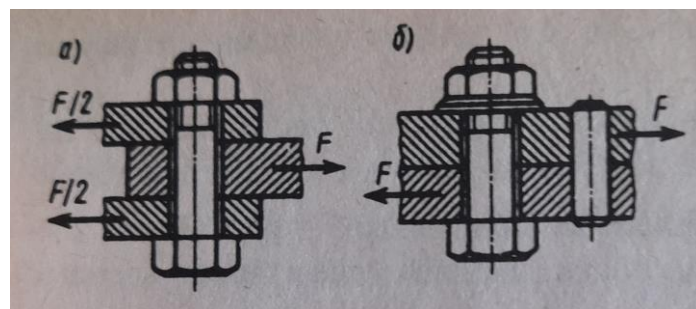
Расчетные схемы болтовых соединений с зазором, нагруженных поперечной силой
